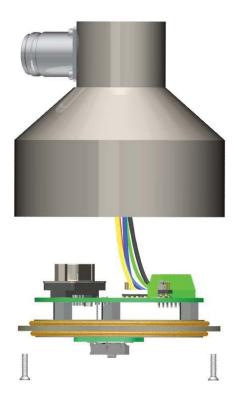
Enlever les 2 vis Philips à tête plate pour exposer la carte de circuit imprimé.
